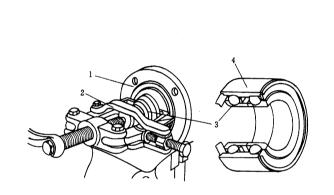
从轮毂上拆下轴承外侧内圈 1. 前轮毂 2. 专用工具 3. 轴承的外侧内圈 4. 双内圈轴承
